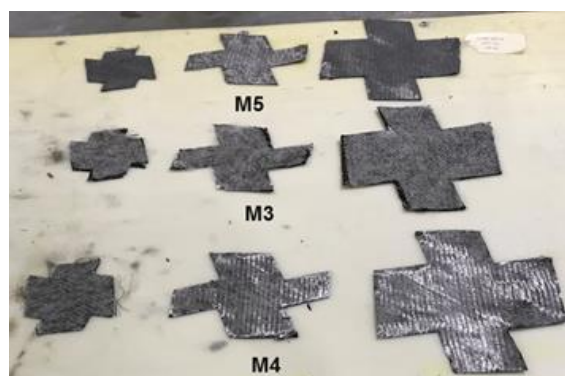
1ª, 2ª e 3ª camadas de topo dos diferentes fornecedores após corte em máquina de corte automático.
